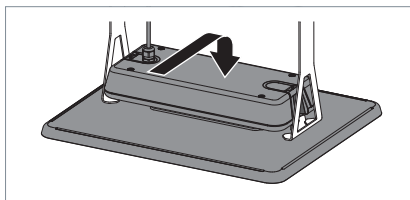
Accrocher le luminaire à la fixation au plafond.
